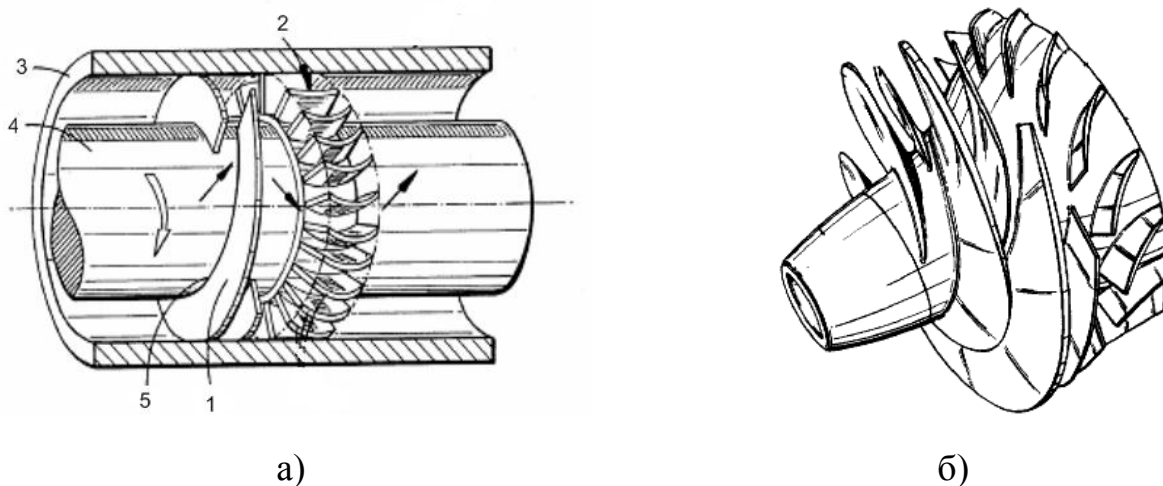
Осьові проточні частини а) ступінь осьового насоса для перекачування багатофазних рідин [33]: 1 – робоче колесо, 2 – статорний апарат, 3 – корпус, 4 – вал, 5 – втулка; б) зовнішній вигляд ступеня для перекачування пульпи та вугілля [34]
